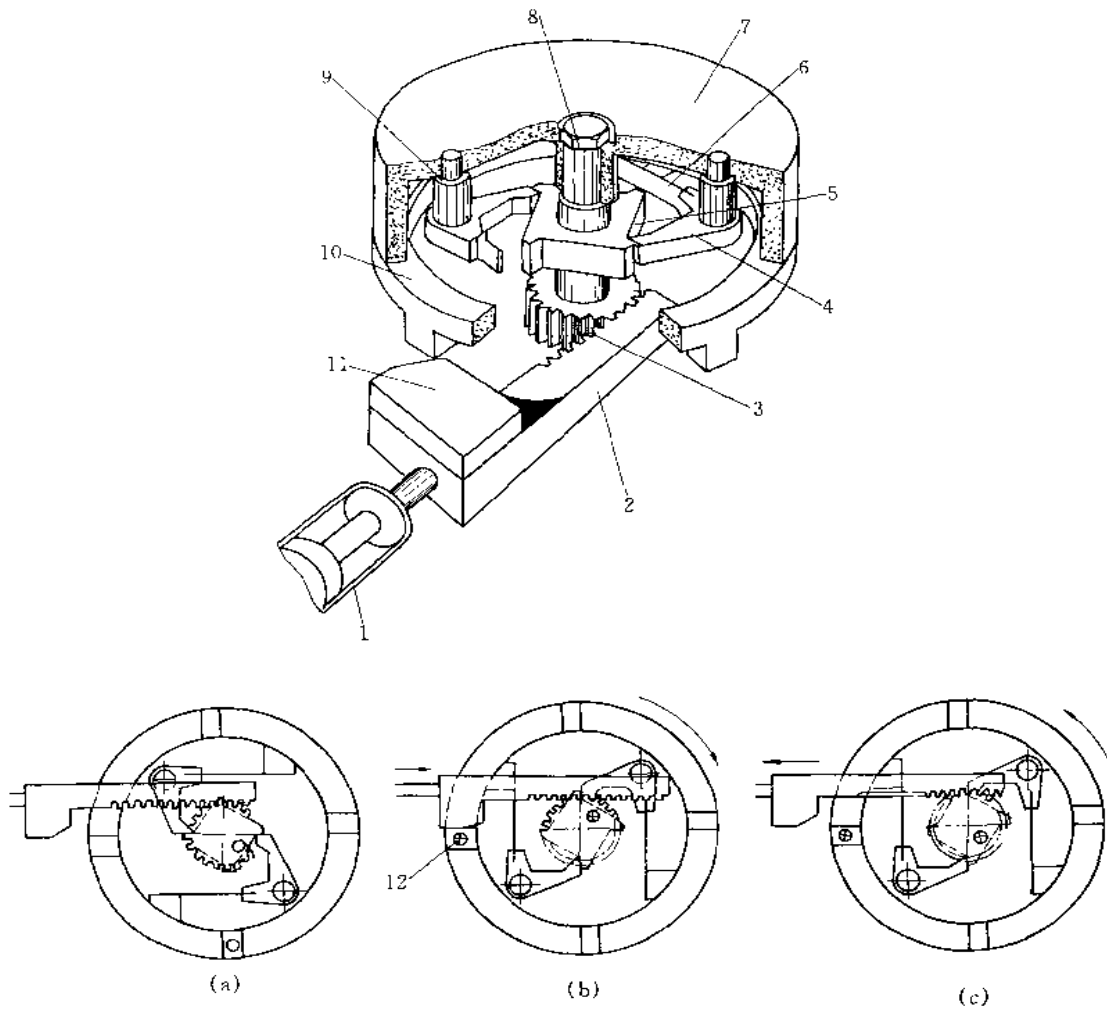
用棘轮-齿轮齿条机构的转位机构
